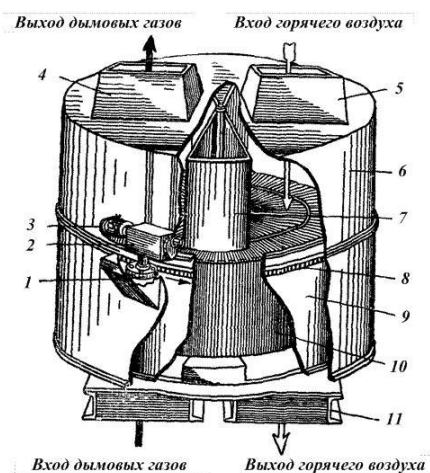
Регенеративный воздухоподогреватель (общий вид):
